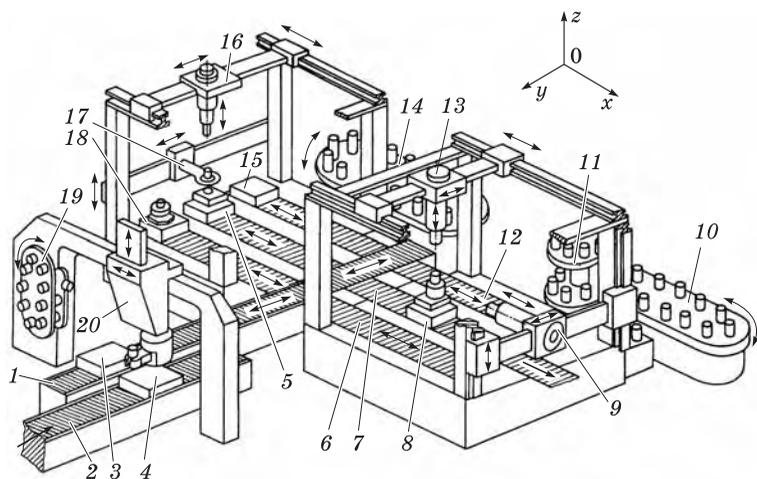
Двухпозиционный сборочный центр для параллельной сборки двух изделий
